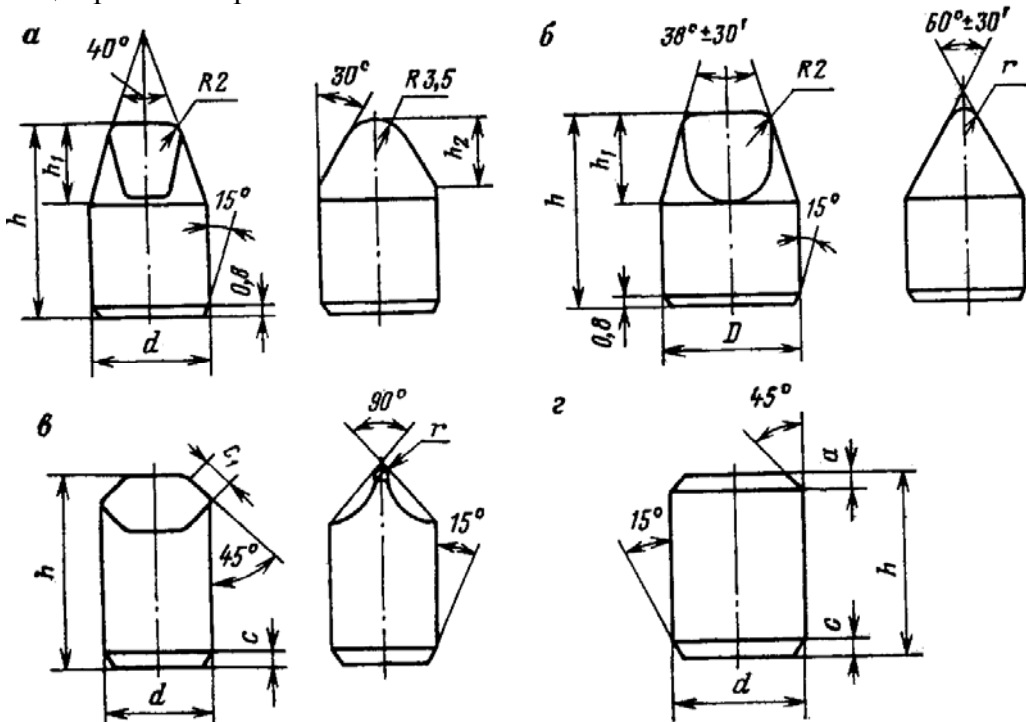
Элементы вооружения долота типа МЗ: а – зубок М; б- зубок М2; в- зубок Г-25; г – твердосплавная вставка
